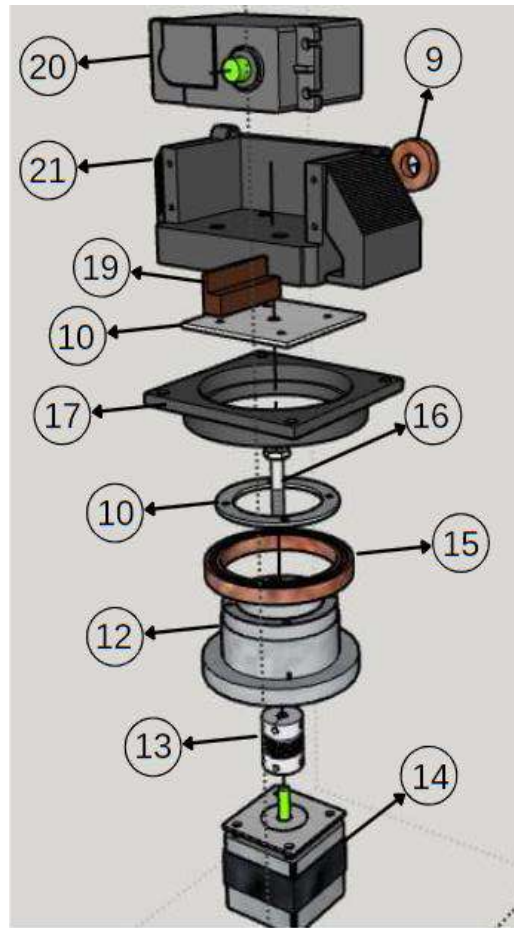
Diseño 3d hombro-cintura vista explotada
